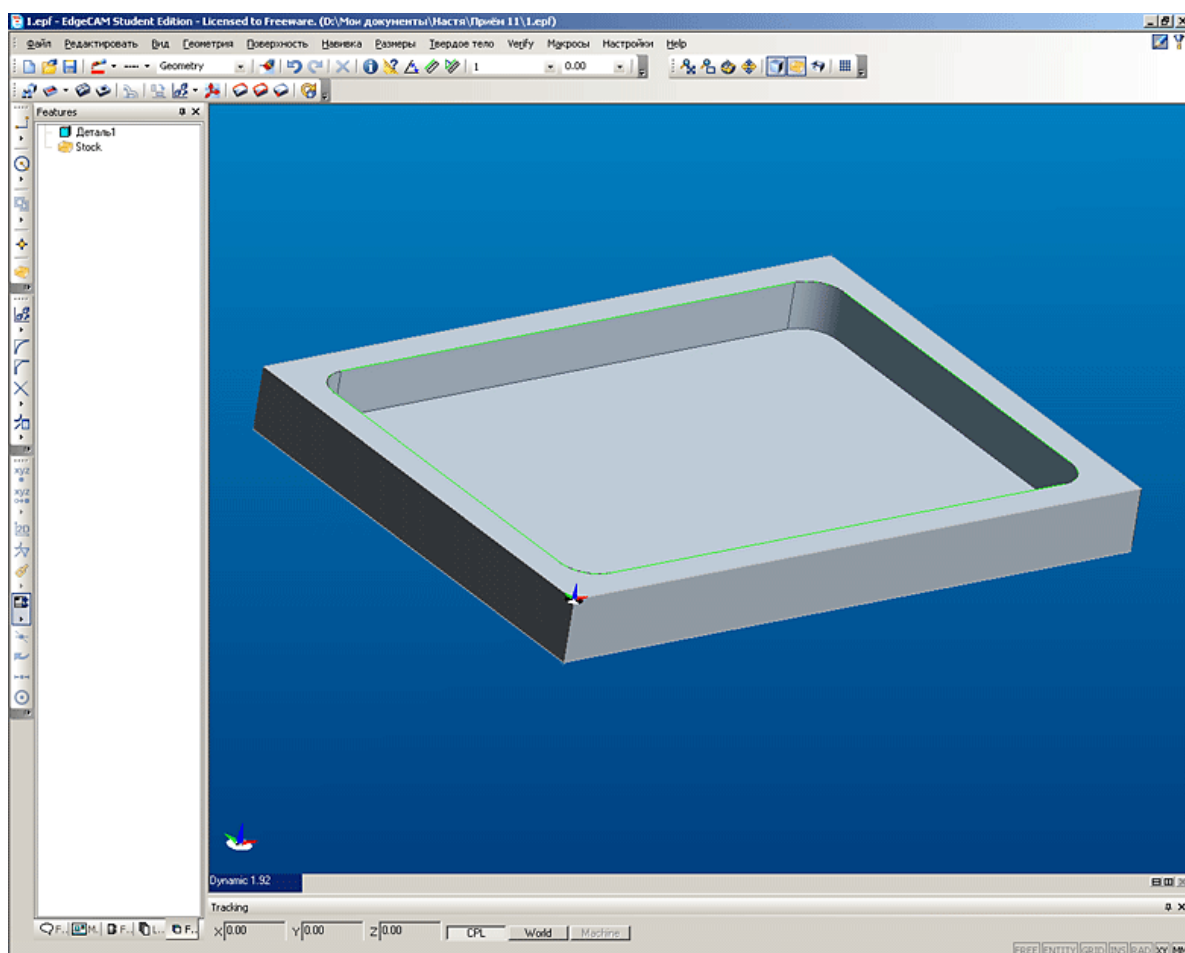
Edgесam. Деталь с созданной ПСК и заготовкой.
